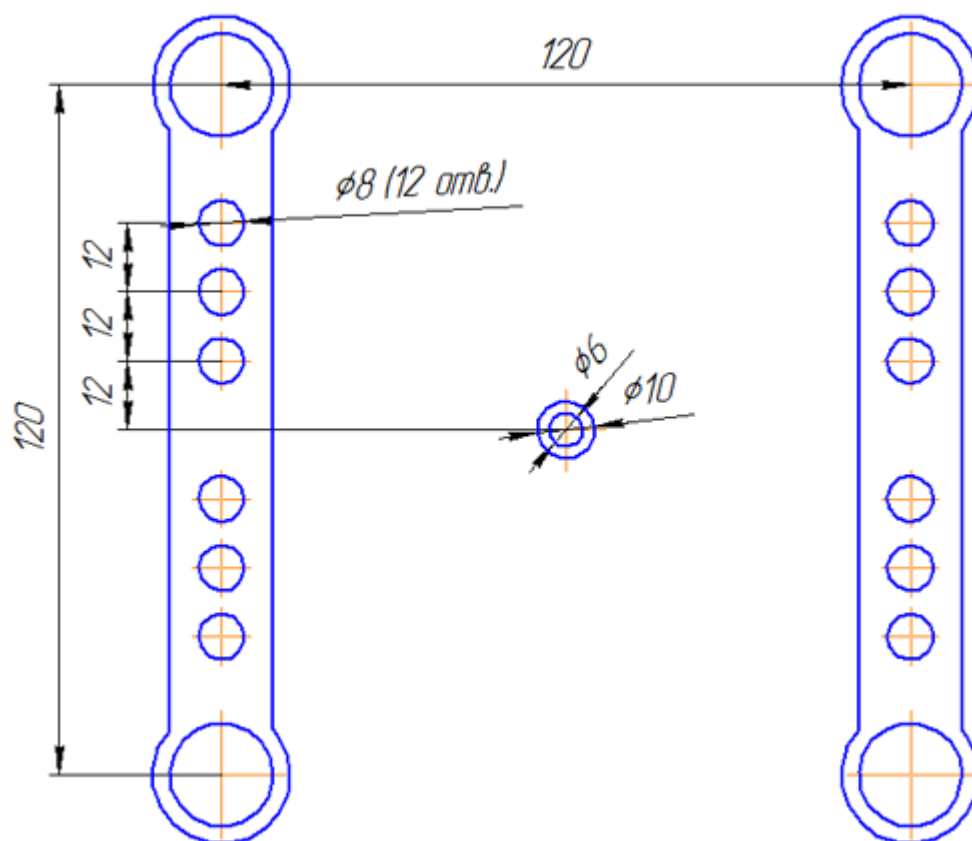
Присоединительные размеры для установки формообразующей детали
